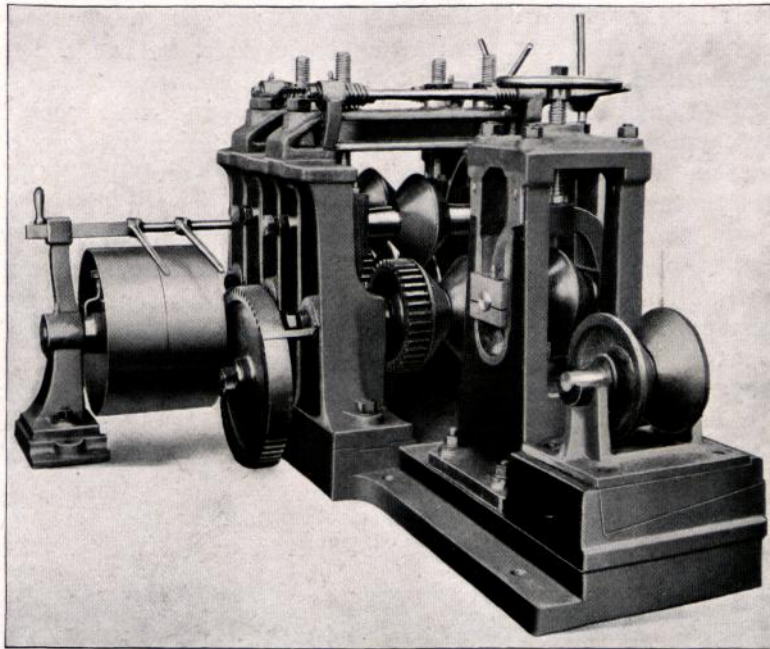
Ansicht einer Rollenrichtmaschine für Winkeleisen. Kalker Werkzeugmaschinen-Fabrik Breuer, Schumacher & Co. A.-G. Kalk bei Köln.
